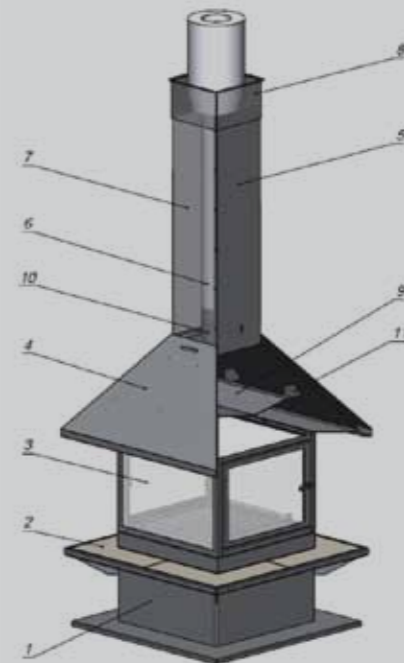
основание; 2 – плитка керамическая; 3 – корпус камина; 4 – кожух; 5 – кожух-ограждение трубы; 6 – трубы дымохода; 7 – кожух-ограждение; 8 – верхнее ограждение труб; 9 – рассеиватель; 10 – шибер (заслонка); 11 – кронштейн.
